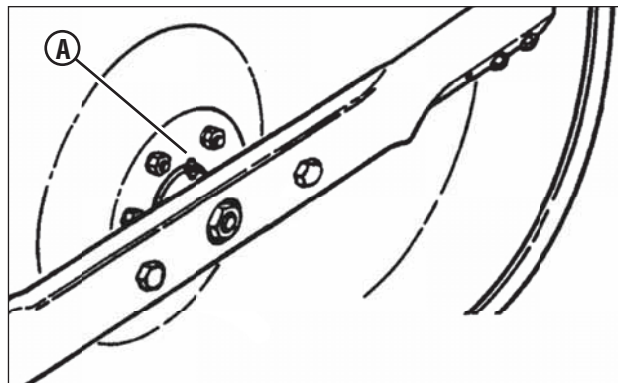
Ponto de engraxe do eixo da lâmina do cortador
